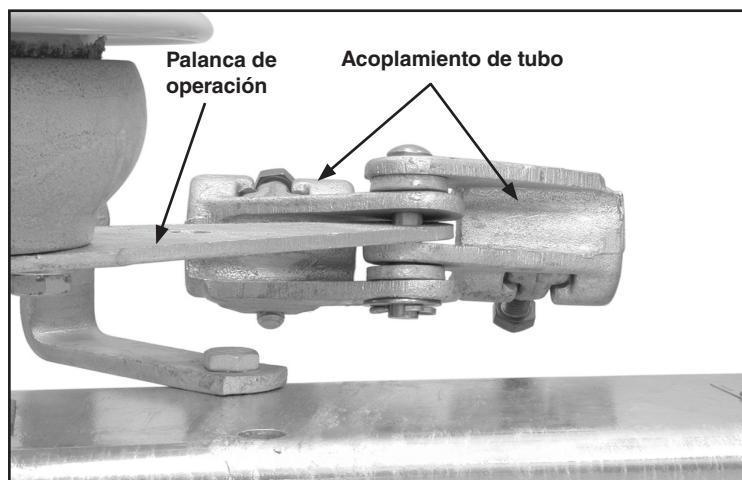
Ensamblaje del acoplamiento de tubo a la palanca de operación—tubo de interconexión a ambos lados de la palanca de operación.
